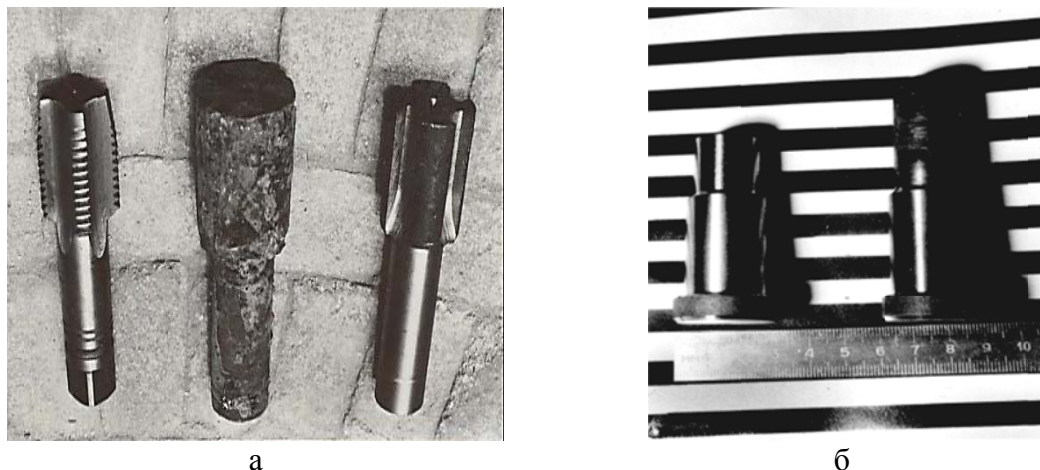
Внешний вид заготовок наплавленного (а) и готового инструмента (б)
